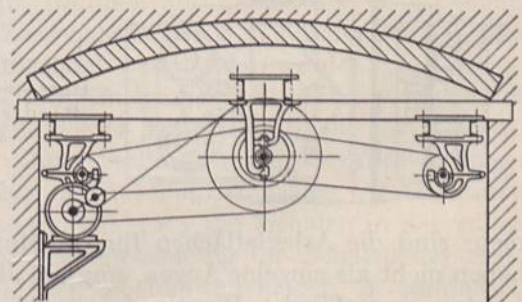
Einbau eines Triebwerks unter einem Gewölbe.
